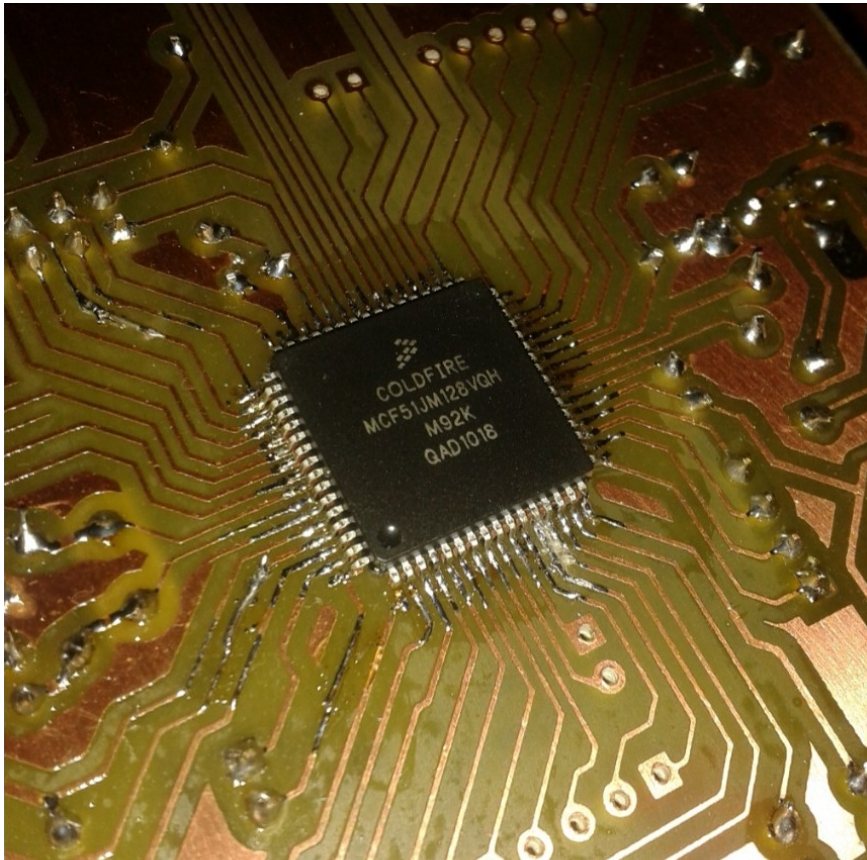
Microcontrolador MCF51JM128 soldado en la plaqueta
